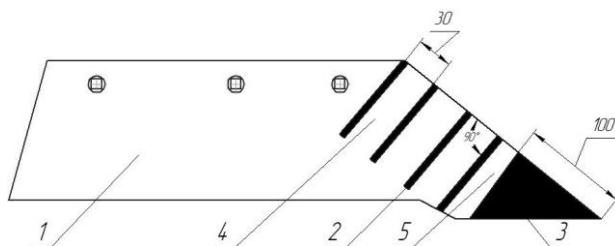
Рабочий орган для подрезания почвы (лемех): 1 – рабочая поверхность; 2 – армирующие валики; 3 – наплавленный дополнительный металл; 4 – область образования лучевидной формы износа; 5 – нижняя часть носка
